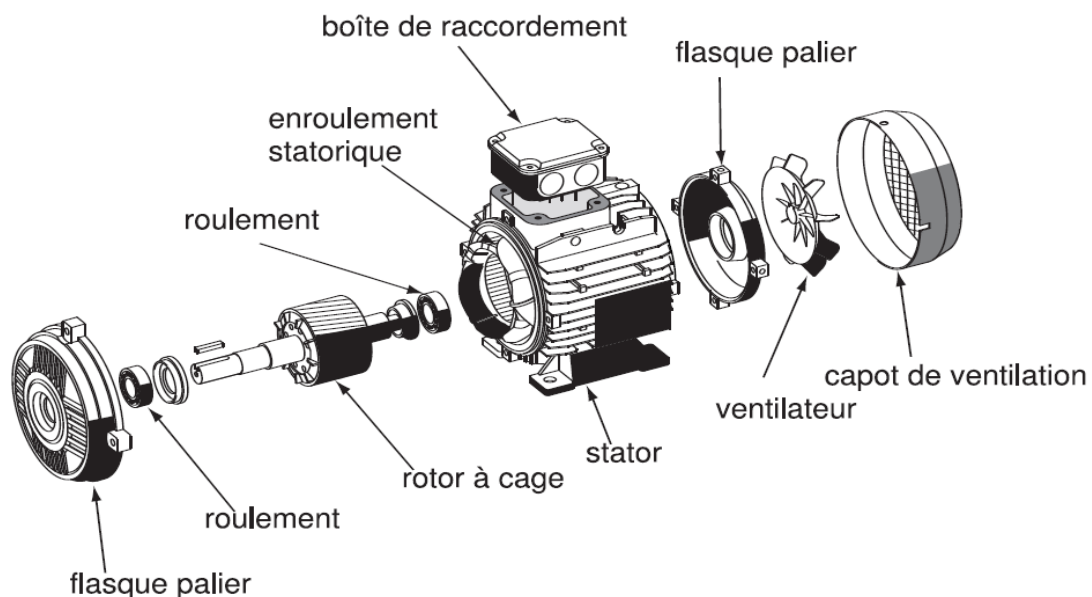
moteur asynchrone à rotor à cage d'écureuil
